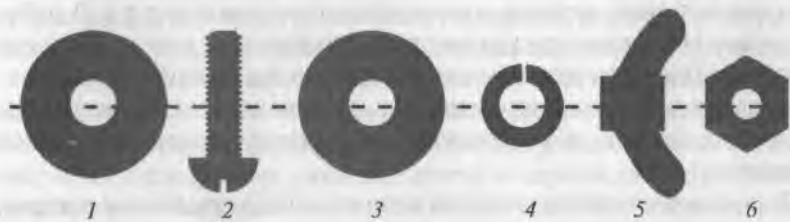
Крепежные детали модели: 1, 3 — шайбы; 2 — болт; 4 — пружинная шайба; 5 — рычажная гайка; 6 — затяжная гайка
